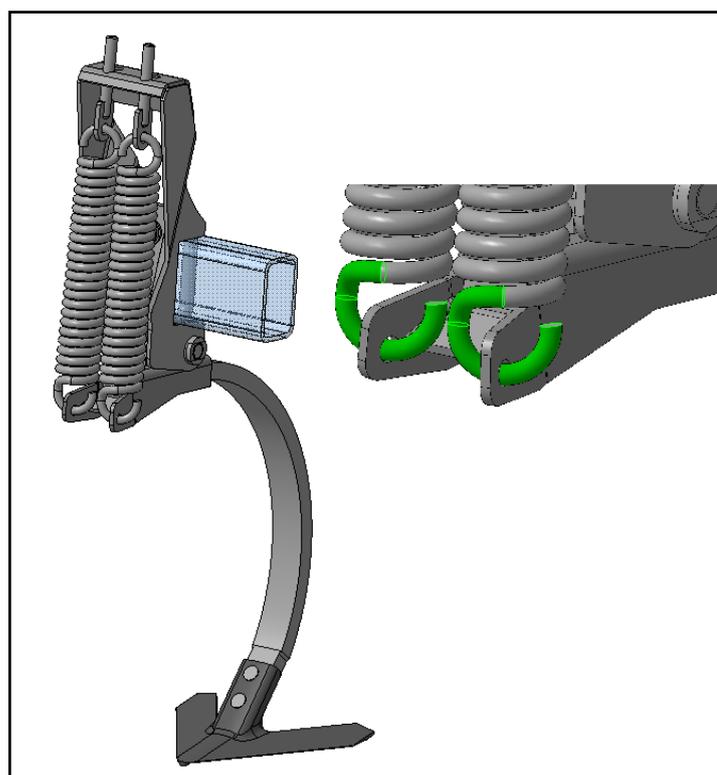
Установка пружин и натяжителей подвески рабочего органа
